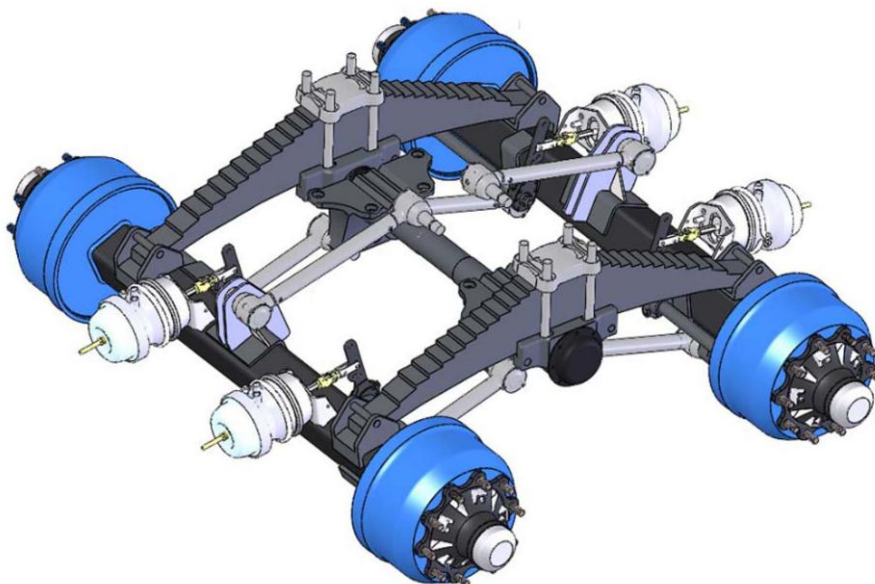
Рессорно-балансирная подвеска с реактивными штангами
